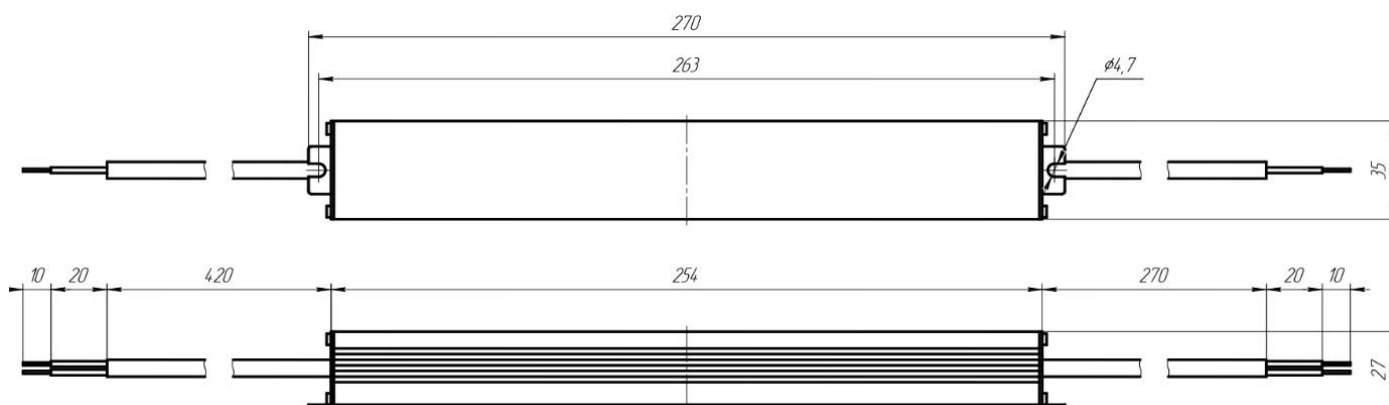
Габаритные размеры Star 100-700T Industrial и Star 130-700T Industrial
